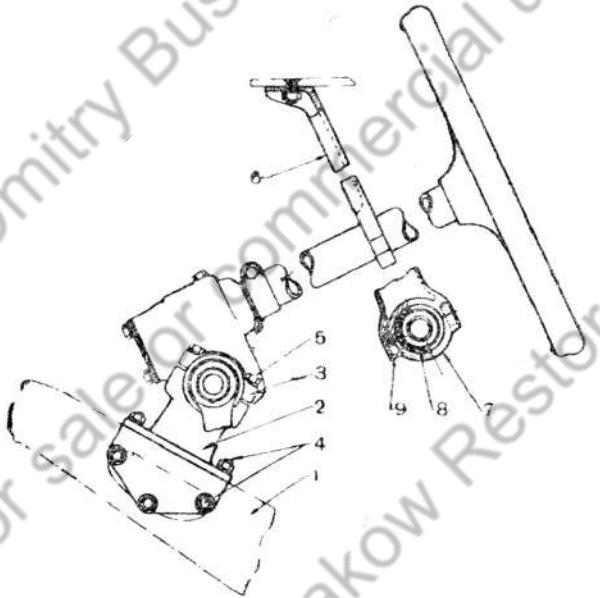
Крепление рулевого механизма к раме и корпусу:
